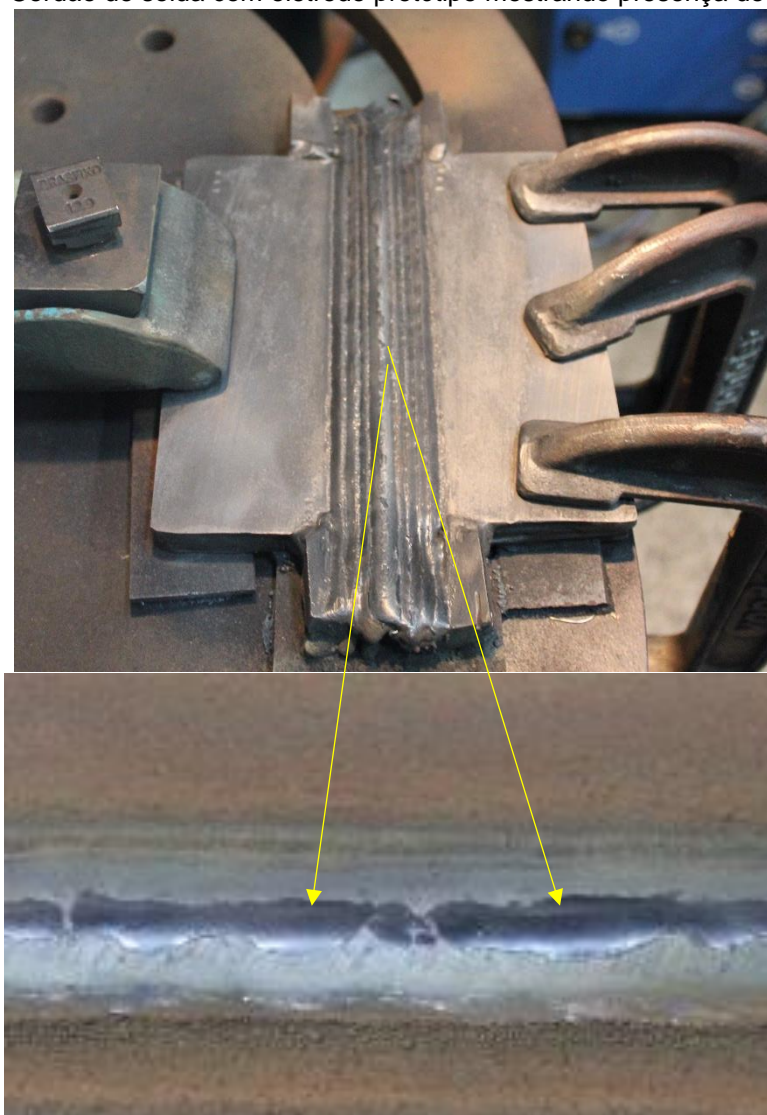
Soldagem Dissimilar: Imagens dos cordões de solda.
